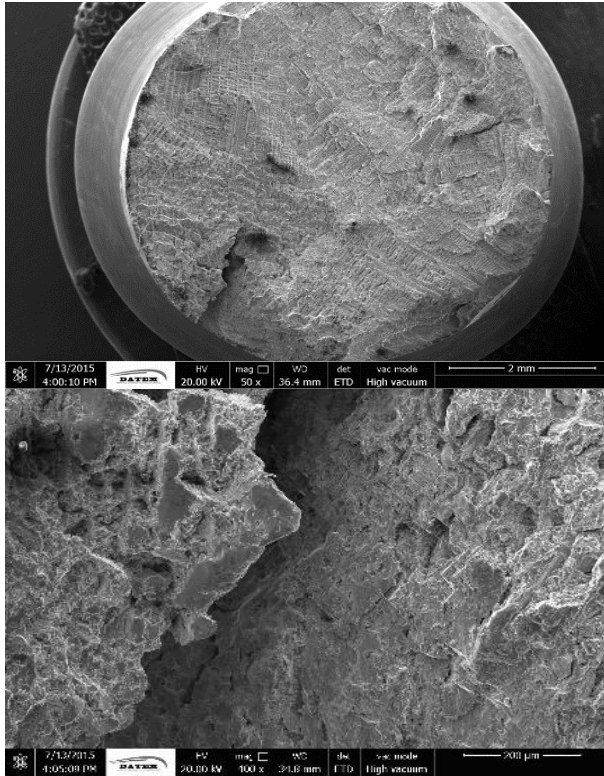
VD225 kodlu parçanın kırılma yüzeyi görüntüleri (Images of fracture surface of VD225 coded sample)
